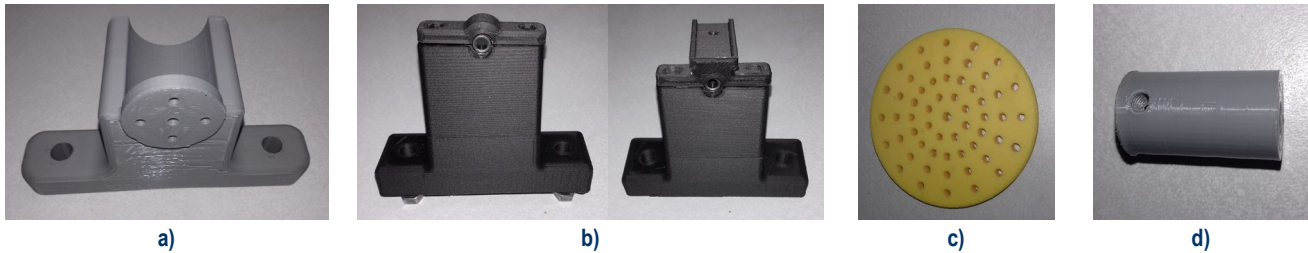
Partes del sistema manufacturadas: (a) Soporte motor DC; (b) Chumaceras; (c) Disco; (d) Cople.
